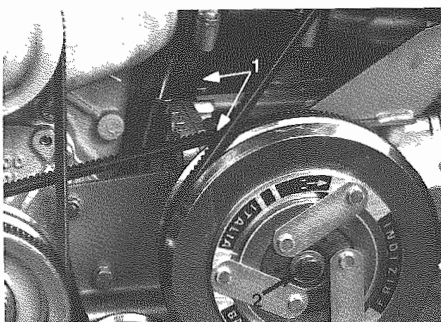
1) Viti fissaggio compressore - Compressor screws
